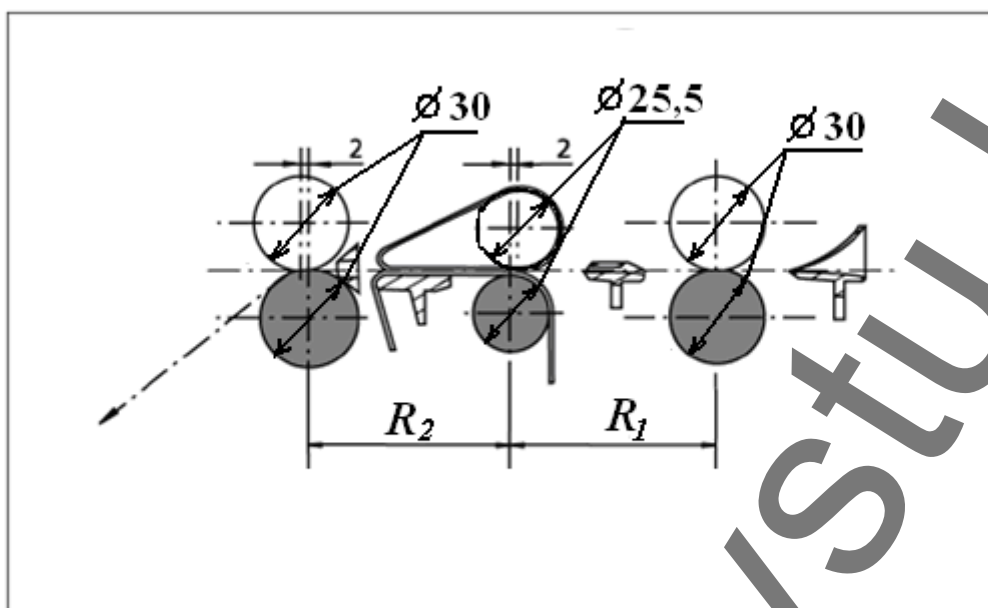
Трехцилиндровый двухремешковый вытяжной прибор на ровничной машине мод. 668 ф. Zinser
